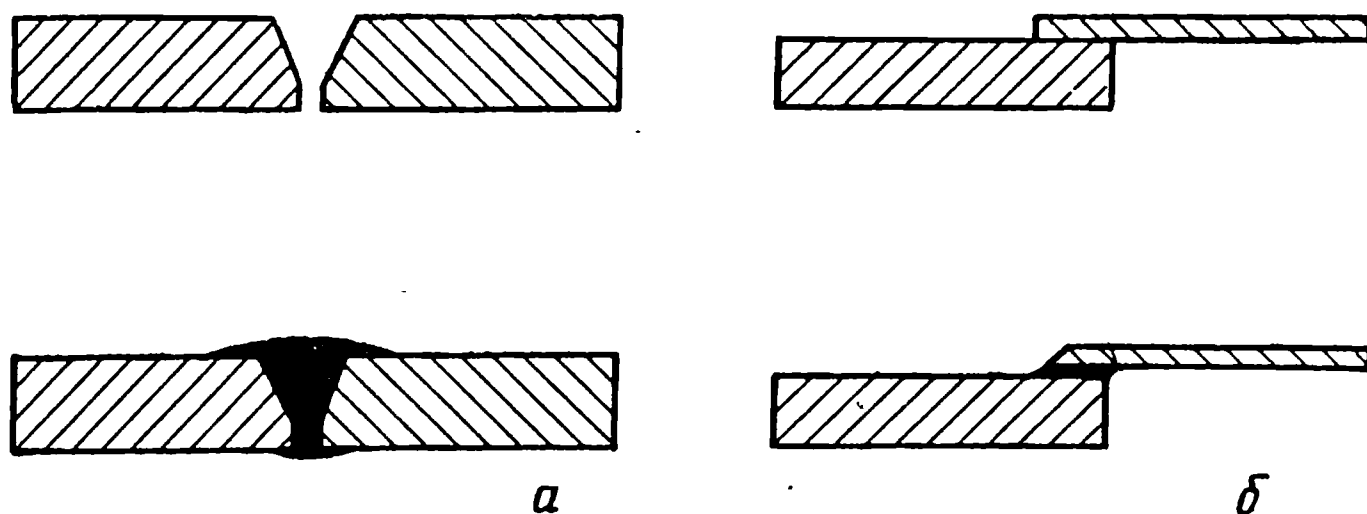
Схема образования шва при пайке-сварке:
